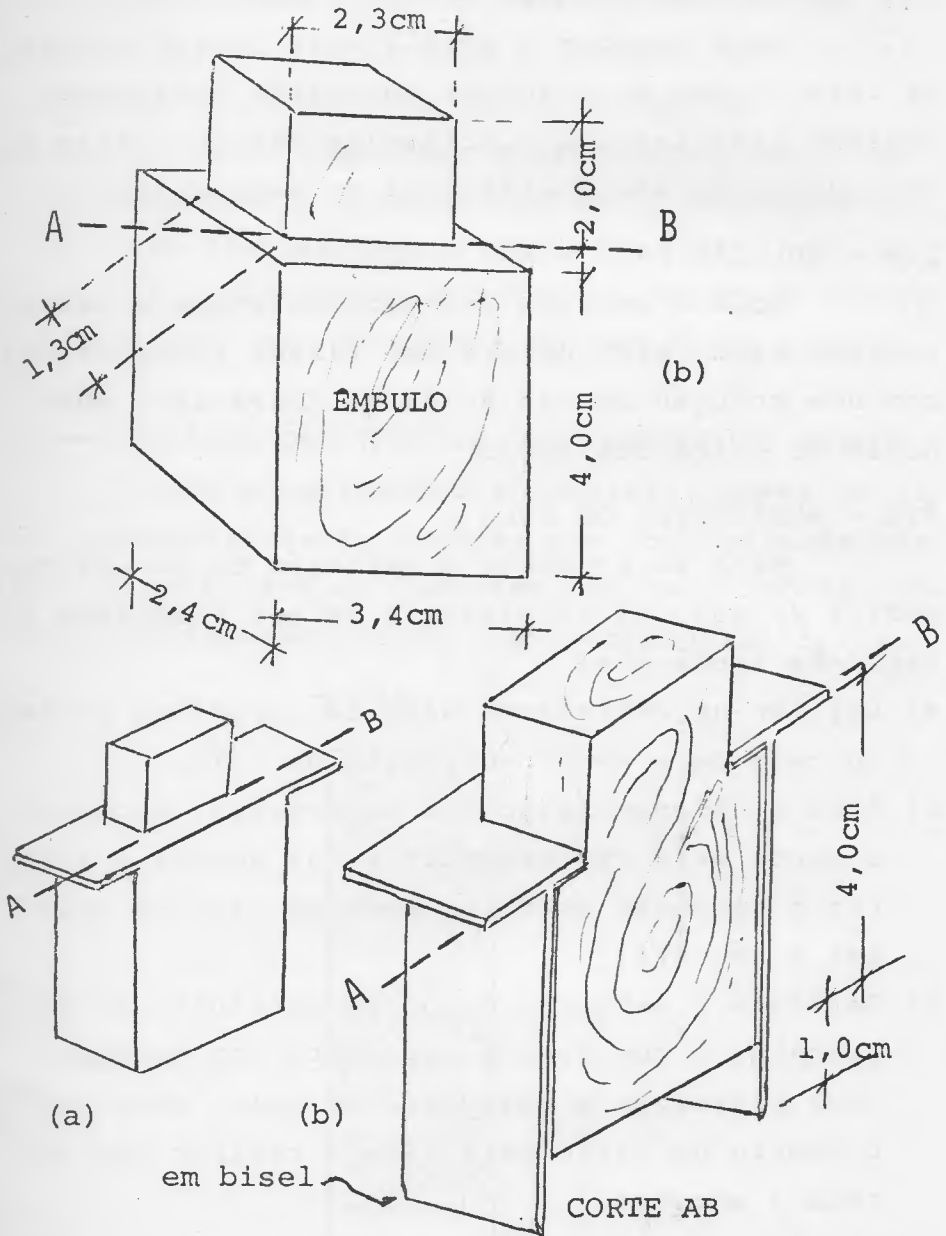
Detalhe do extrator; (a) extrator; (b) êmbulo; (c) corte AB
